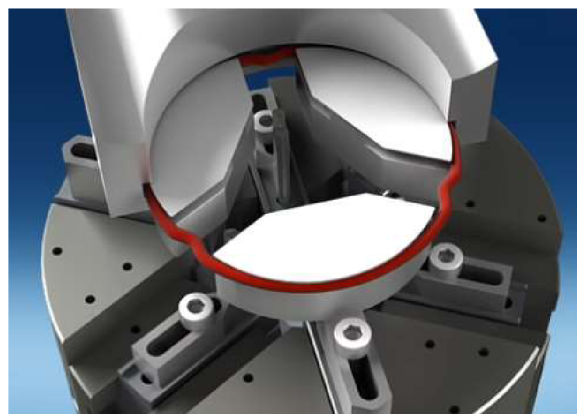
1. Nájezd k o-kroužku pro uchopení [10]
